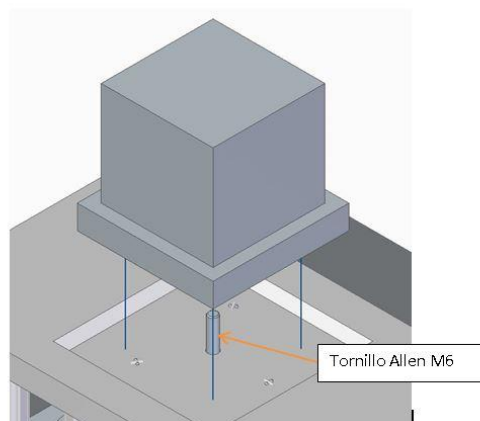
Proceso de montaje de la pieza sobre la mesa de trabajo y la posición de su componente.
